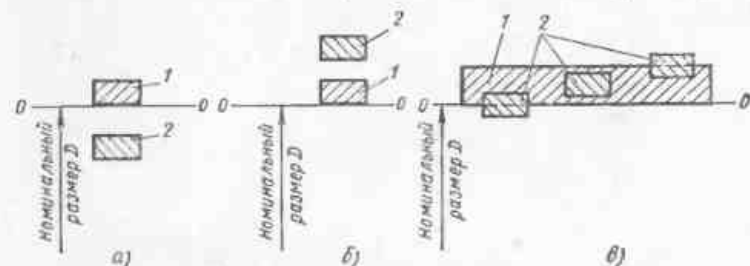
Расположение полей допусков посадок: а — с зазором; б — с натягом; в — переходных; 1 — поля допусков отверстий; 2 — поля допусков валов
